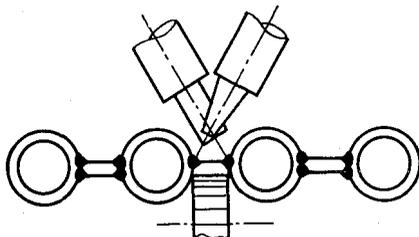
Схема сварки полосы между гладкими трубами (подварочные швы)
